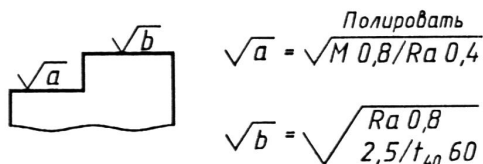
Упрощенное обозначение шероховатости поверхностей
